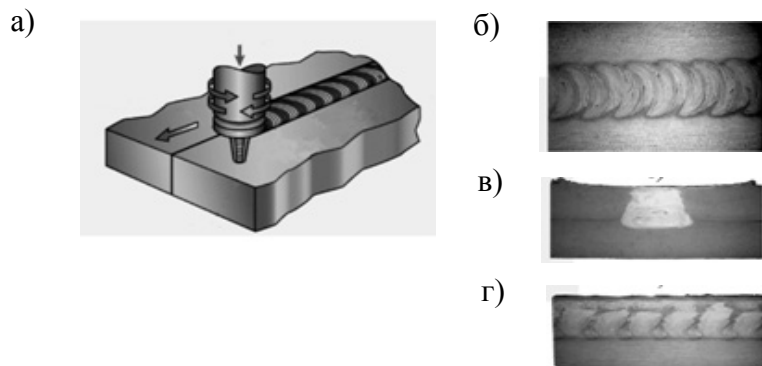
СТП с возвратно-вращательным движением инструмента: а – схема сварки; б – вид сварного шва; в – сечение перпендикулярное направлению шва; г – сечение вдоль шва
